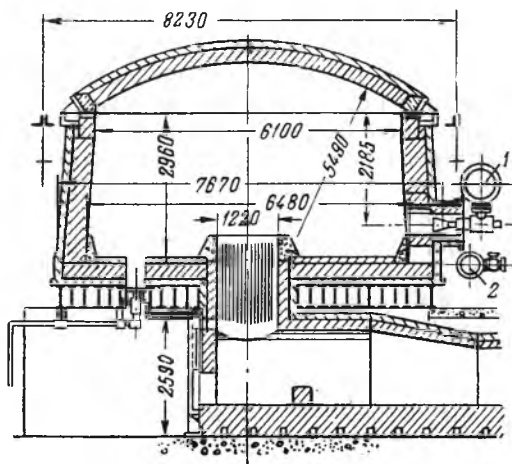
Колодцы с круглой камерой без подогревателей: 1 — воздух; 2 — газ
